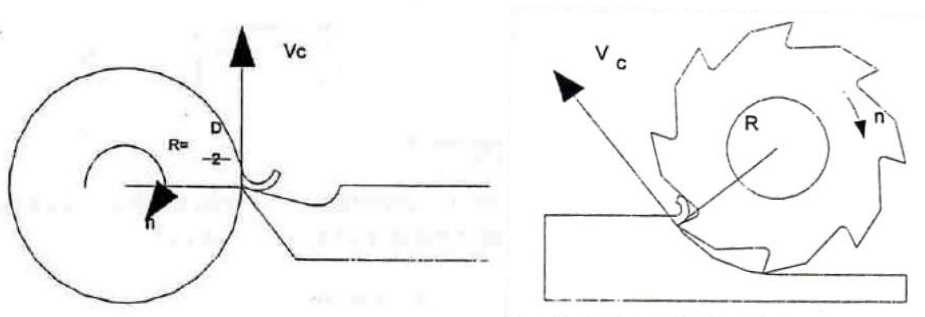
Velocidad de corte en torneado y fresado [12].
